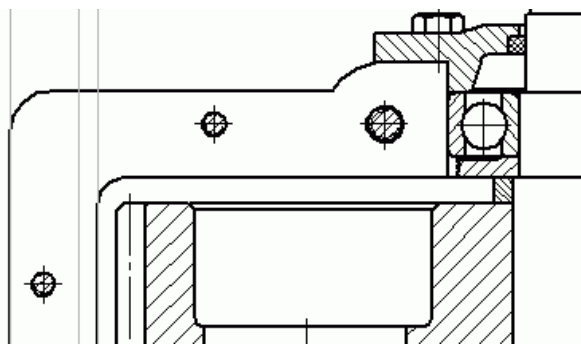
Вспомогательные линии для построения корпуса редуктора
